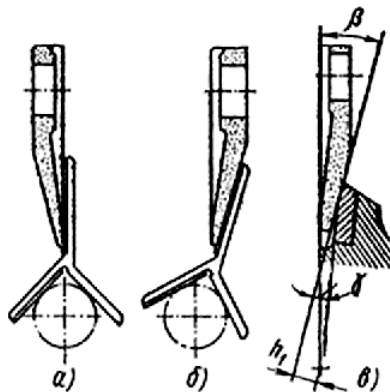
Установка шлифовального круга при заточке передней поверхности инструмента:
